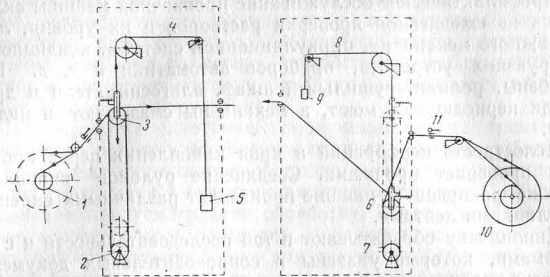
Схема загрузочного и разгрузочного магазинов:
